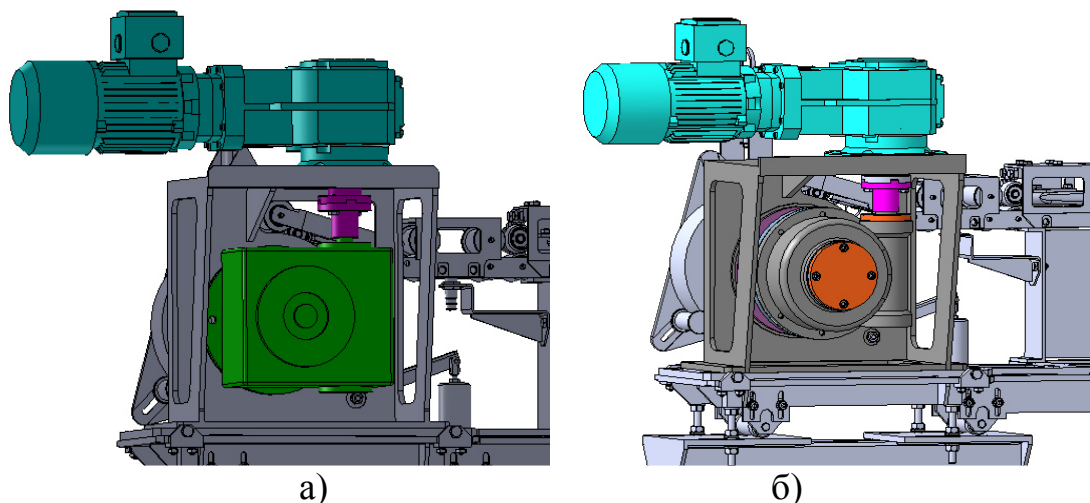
Схема привода а) исходный привод, б) предложенный привод
